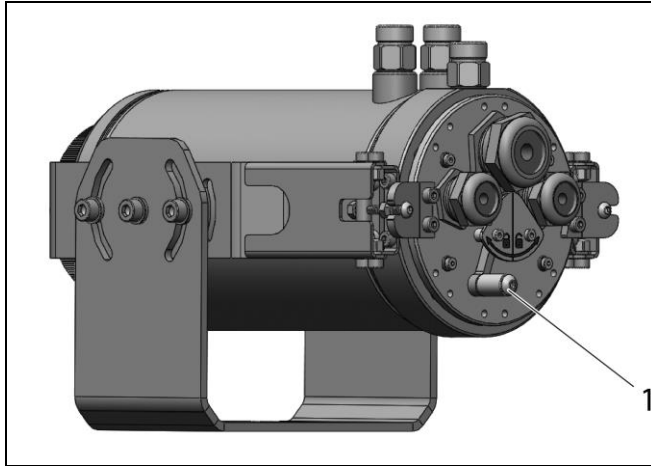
Rückansicht Cooling Jacket mit Verriegelungshebel
